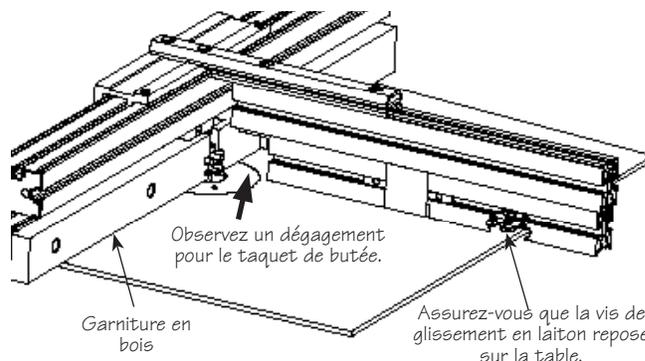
Positionnement du guide perpendiculaire pour l'usinage en bois de bout.
